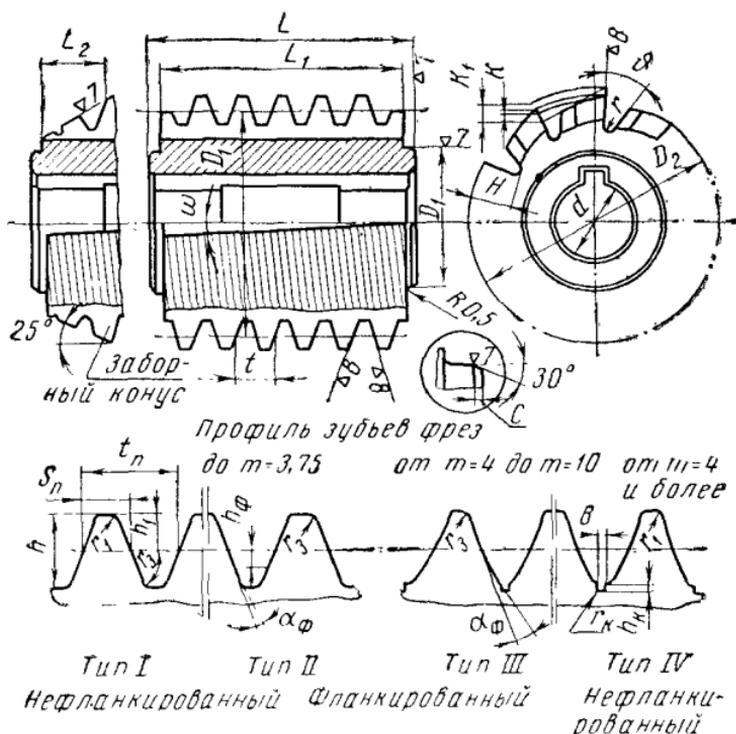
Общий вид червячной фрезы для нарезания зубьев цилиндрических зубчатых колес
